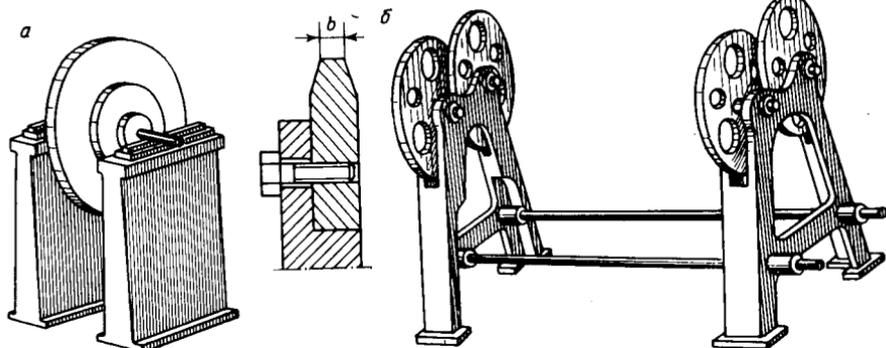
Приспособления для статической балансировки валов; а — призмы; б — диски.
